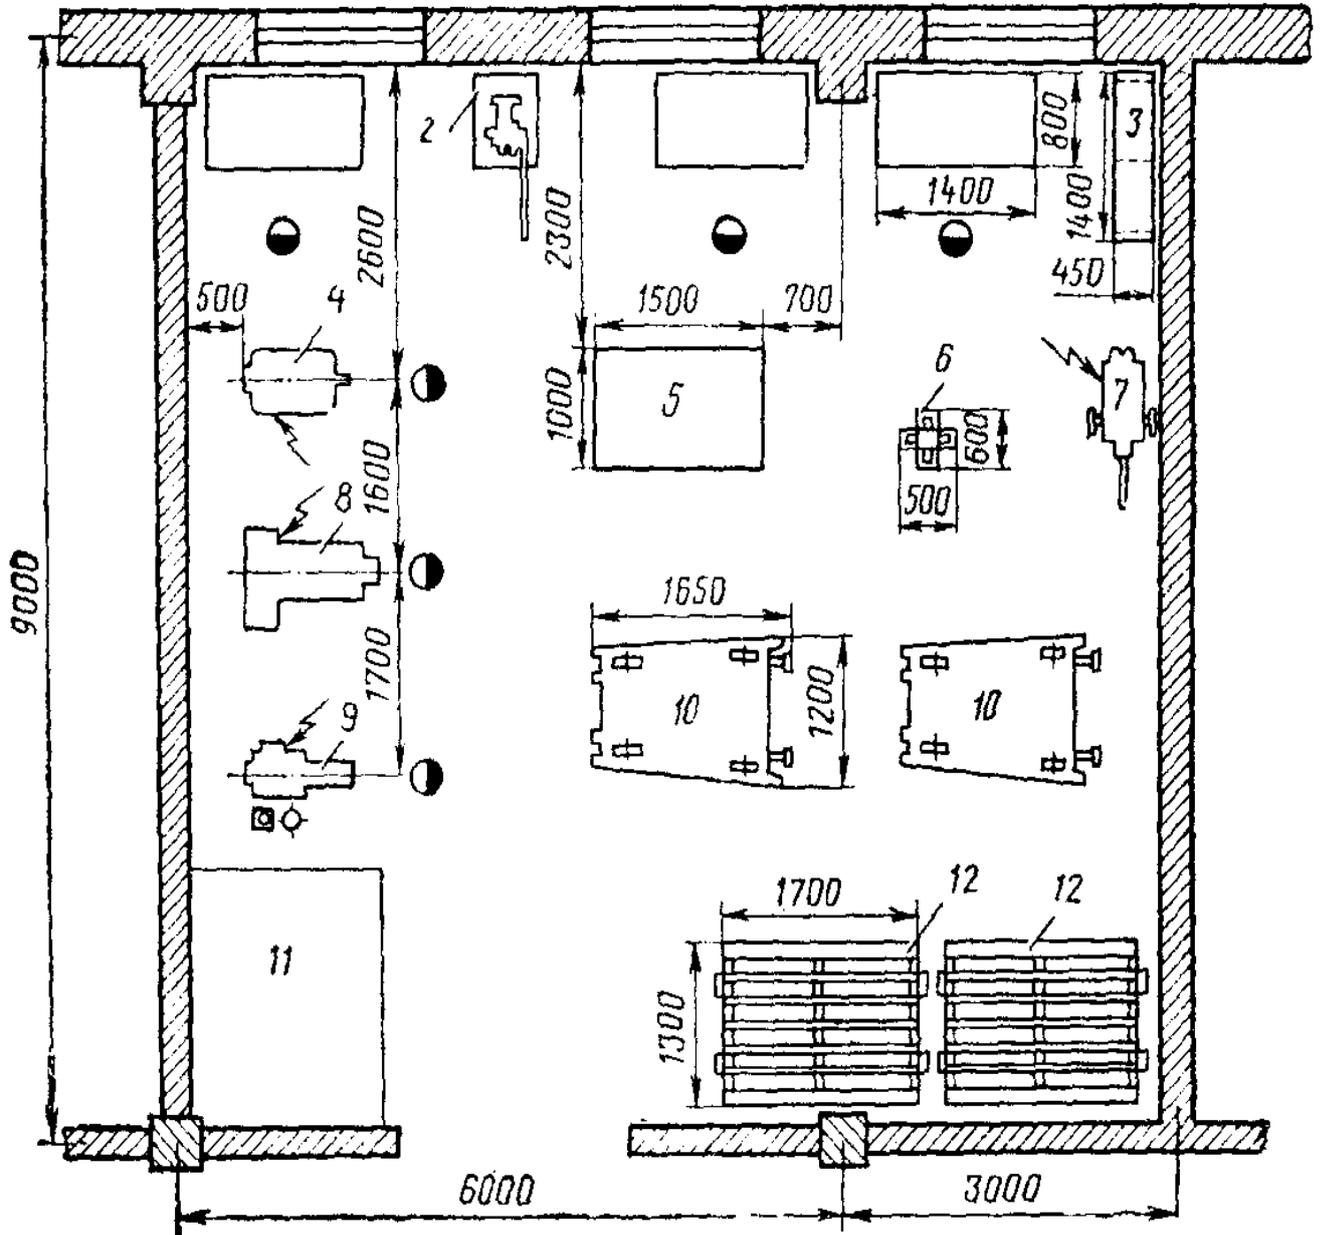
Технологічне планування бляхарського відділення: 1 — верстаки; 2 — ножиці; 3 — стелаж; 4 — станок вертикально-свердильний; 5 — плита рівняльна; 6 — стенд для ручного рихтування; 7 — станок шліфувальний; 8 — зиг-машина; 9 — установка для зварювання; 10 — візок-стенд для ремонту кабін; 11 — місце для зберігання листового матеріалу; 12 — стелажі для крил
